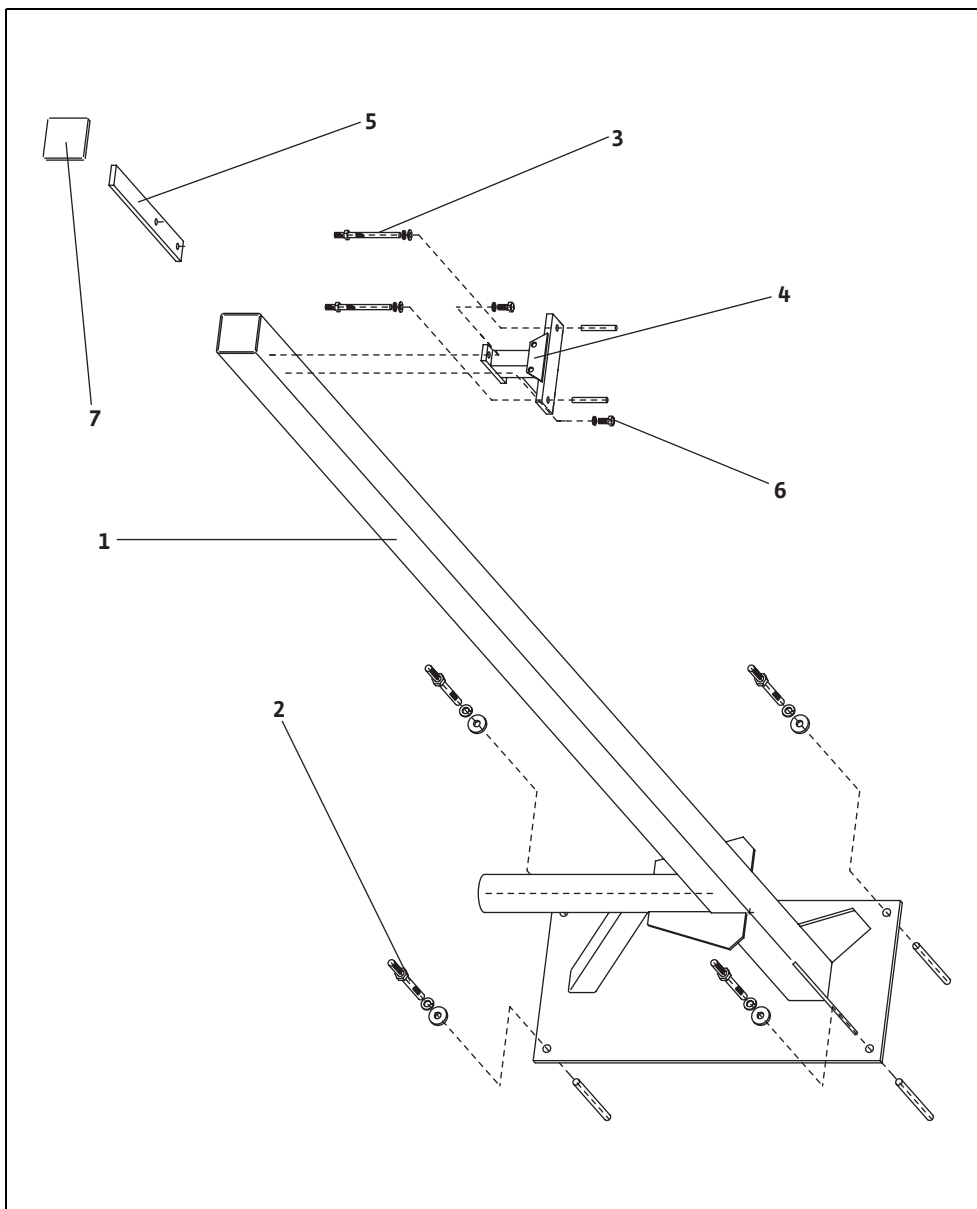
Змонтувати штативний вузол, змонтувати занурювальний пристрій AVUSHH
